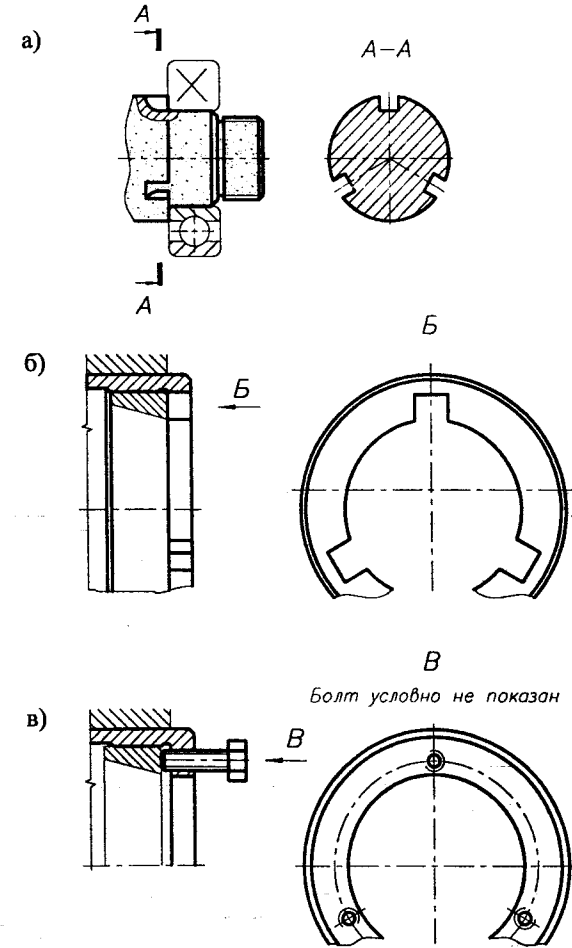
Конструктивные решения по облегчению демонтажа подшипников качения: а), б) выфрезерованные пазы на валу (в корпусе) для возможности захвата лапами съемника боковой поверхности кольца подшипника; в) отверстия с нарезанной резьбой во втулке (корпусе) подшипника для возможности его выжимания из посадочной поверхности.
